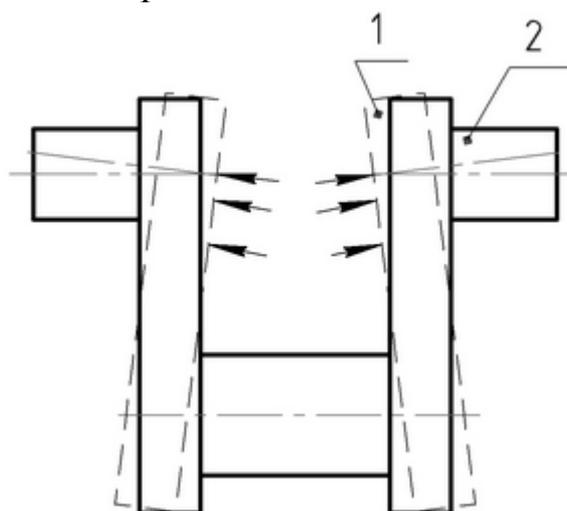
Схема правки коленчатого вала наклепом: 1 – до правки; 2 – после правки
